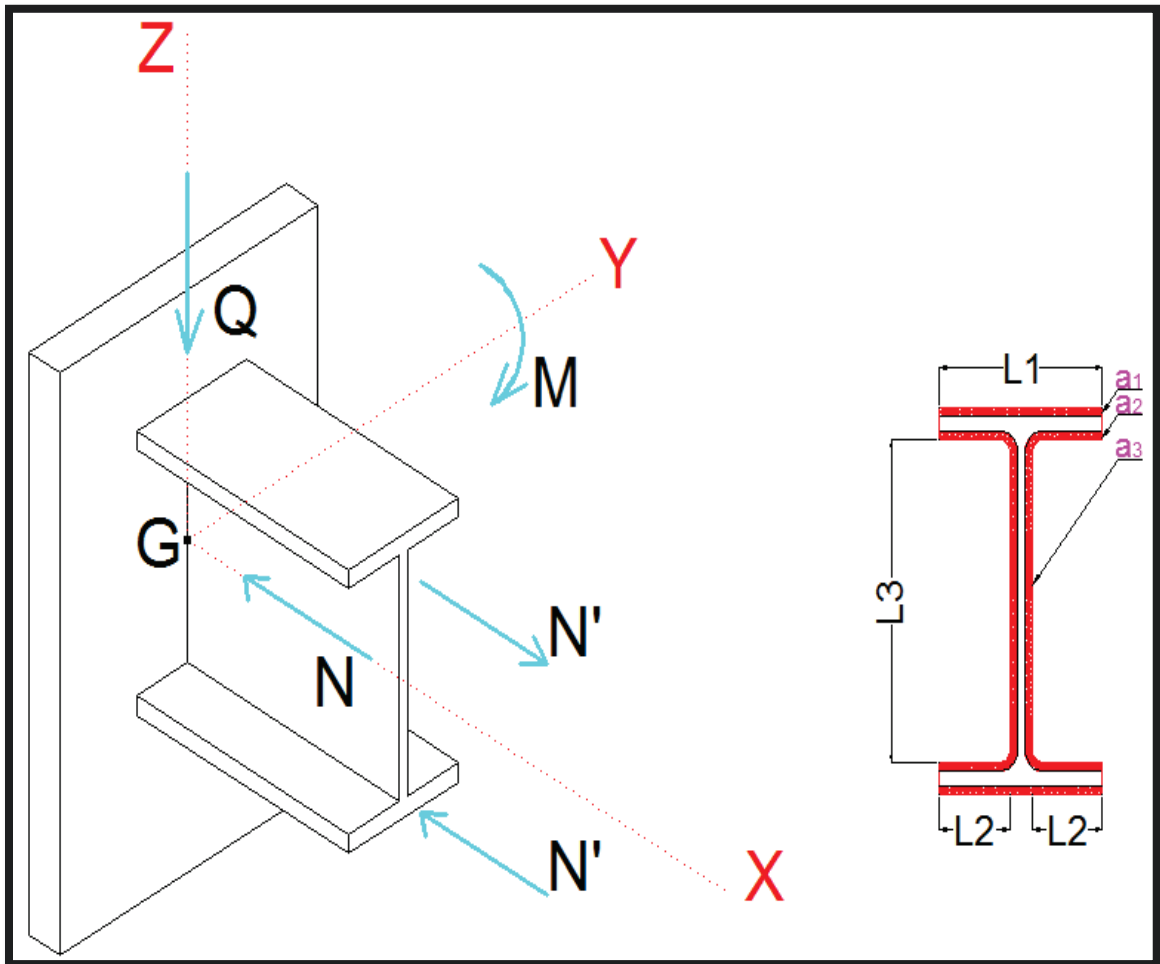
Vue en 3D des sollicitations entre deux pièces soudées
